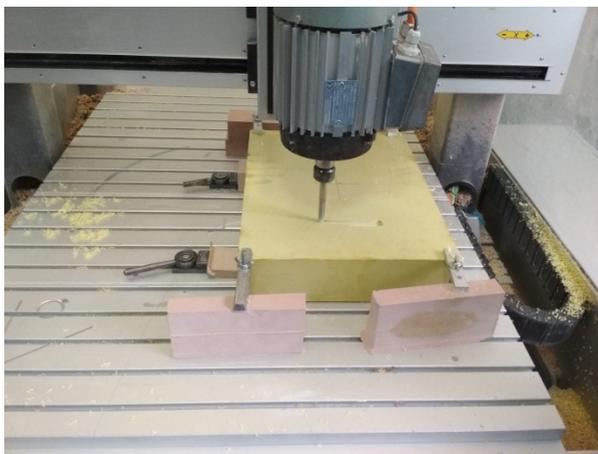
Рабочий стол станка с установленной заготовкой
